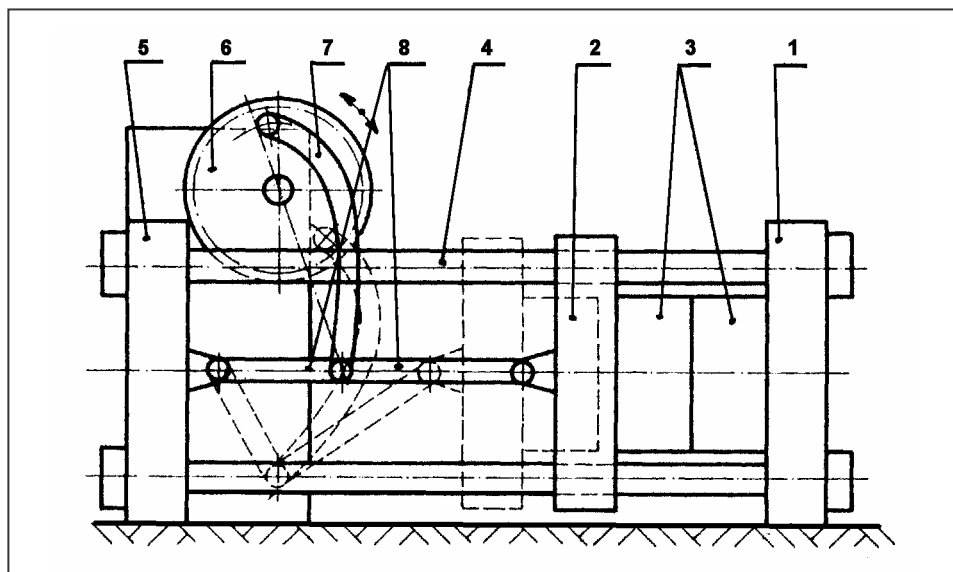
Hydraulicko-mechanické uzavírání s válcem mimo osu stroje
